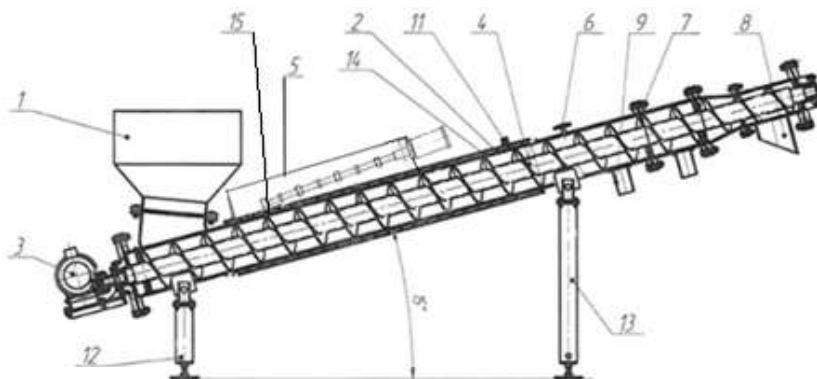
Схема ультразвуковой установки для обработки зерна:
